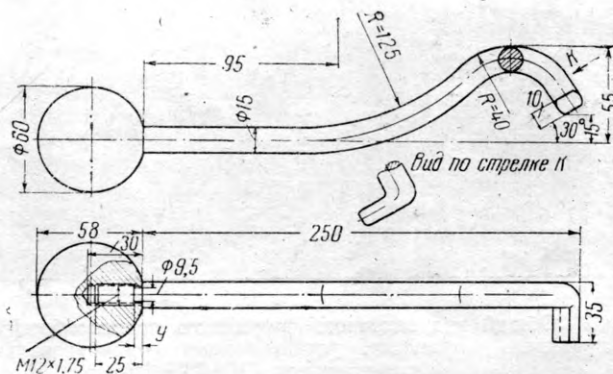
Рычаг для фиксации ножевого вала фуговального станка
